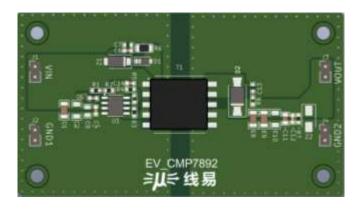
PCB 示意图 (尺寸: 80 x 45mm)
